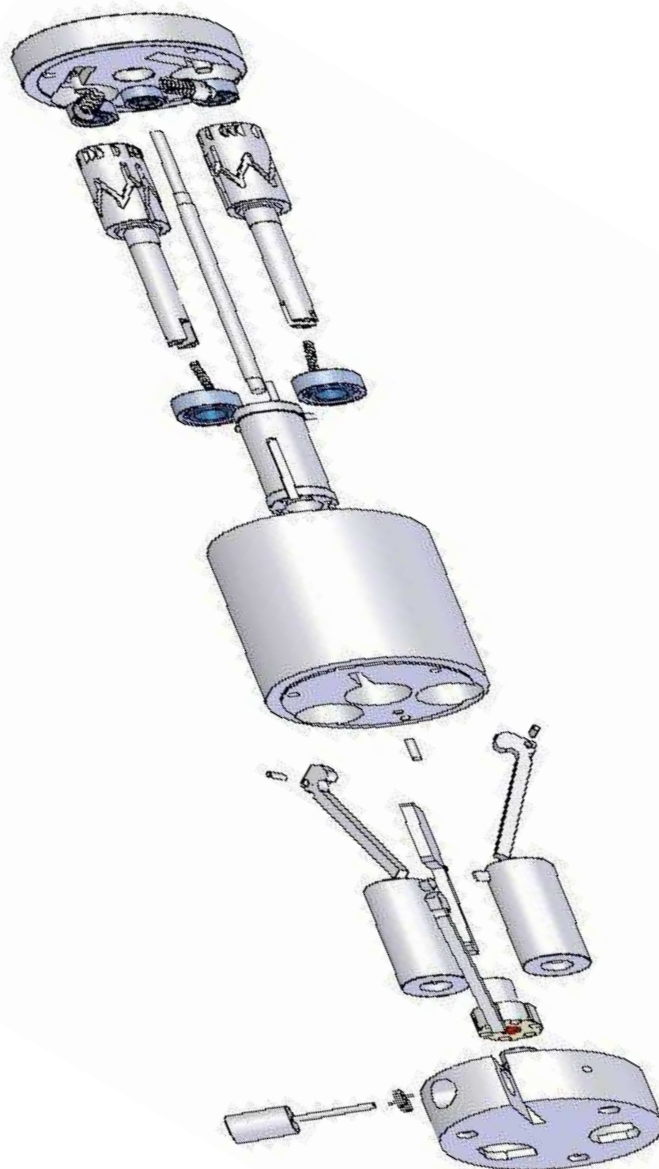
Dispozitivul cu motor electric rotativ pas cu pas, vedere explodată
